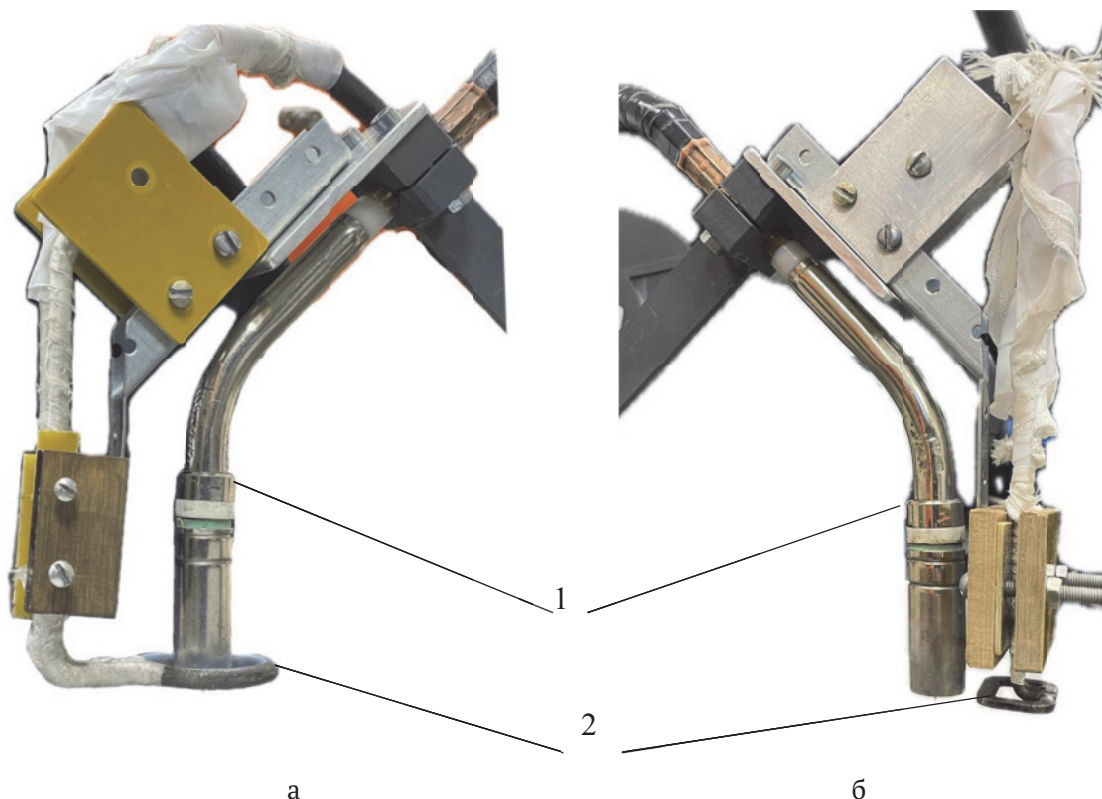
Конструкции индукторов, сопряженных со сварочной горелкой:
